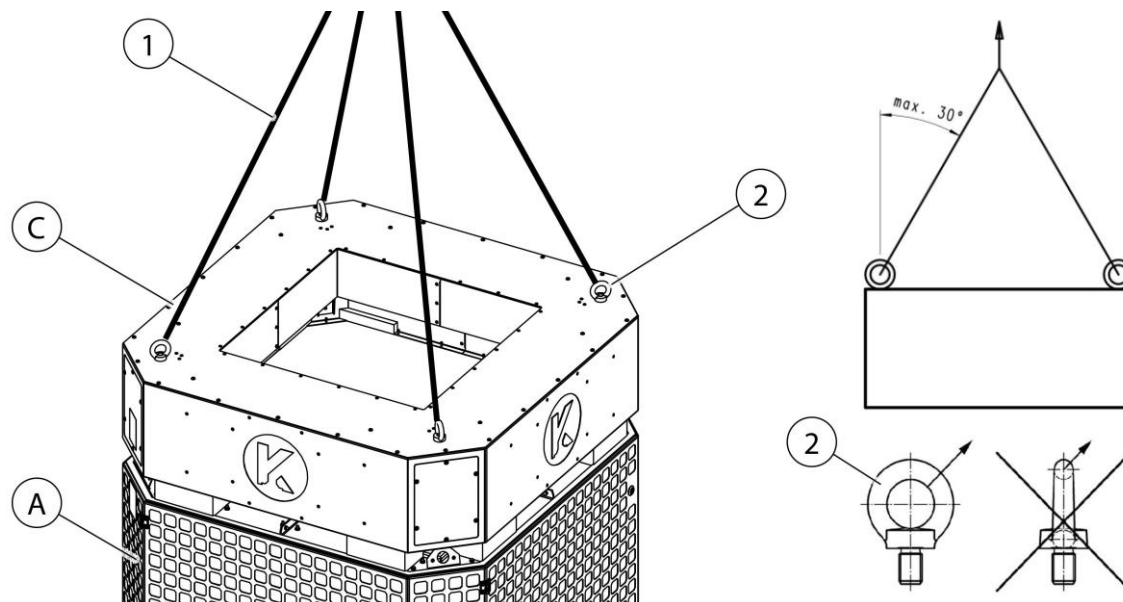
Levage du produit à l'aide d'un pont roulant/dispositif de levage
